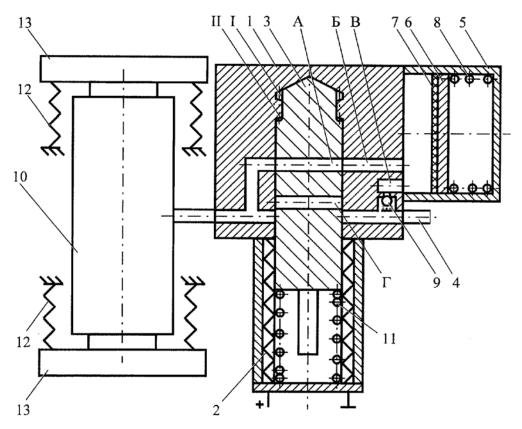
Электромагнитный клапан антиблокировочной системы для гидравлического тормозного привода: 1 — корпус клапана; 2 — обмотки электромагнита; 3 — сердечник; 4 — трубопровод; 5 — дополнительный цилиндр; 6 — поршень; 7 — манжета; 8 — пружина поршиня; 9 — обратный клапан; 10- рабочий гидравлический цилиндр колесного тормозного механизма; 11 — пружина электромагнита; 12 — пружины тормозных колодок; 13 — тормозные колодки
